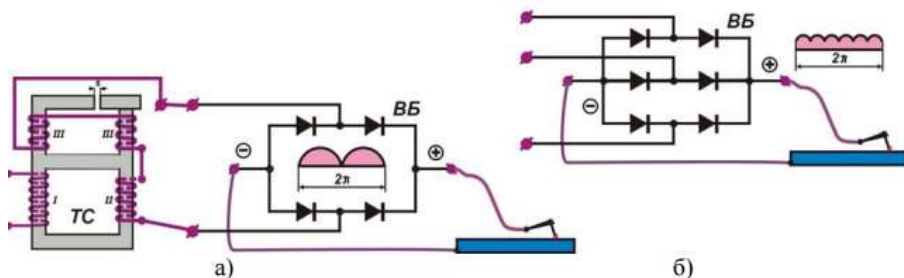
Электрические схемы неуправляемых выпрямителей постоянного сварочного тока. а) при однофазной схеме включения; б) при трехфазной схеме включения. ТС = трансформатор сварочный; ВБ = блок выпрямителя.
